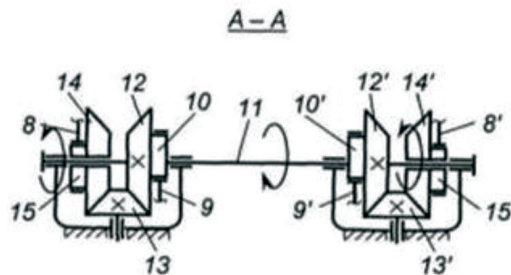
Механізм привода натискної плити з конічними зубчастими колесами
